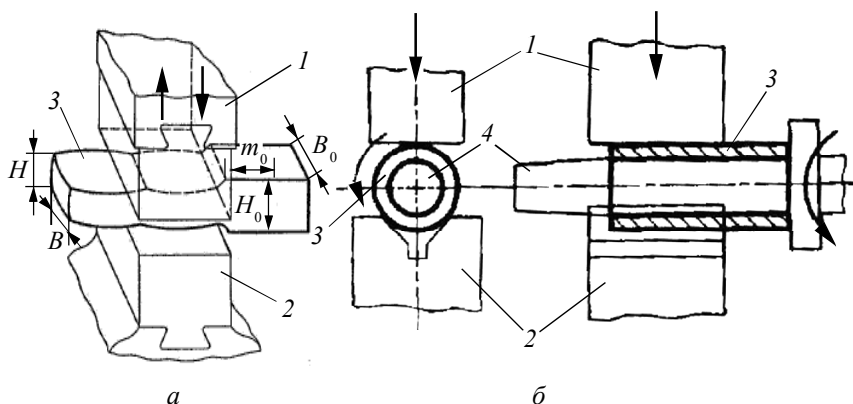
Протяжка кузнечная сплошной (а) и полой (б) заготовки:
